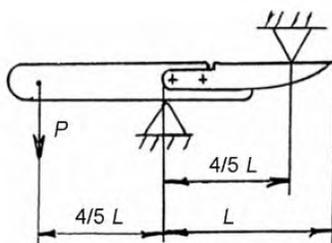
Схема проверки прочности крепления накладных лезвий к корпусу
